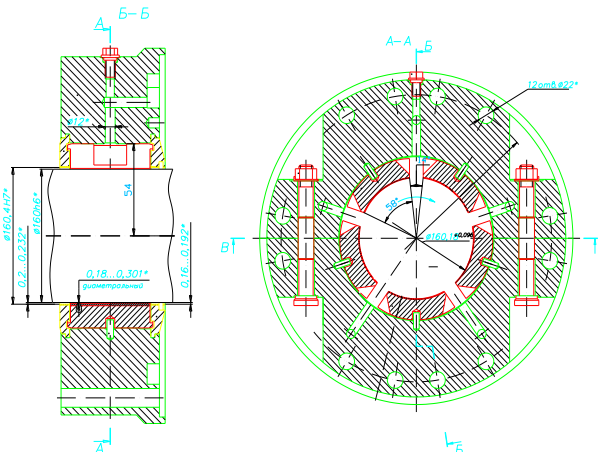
Розрахункова схема п'ятиколодочного підшипника ковзання
